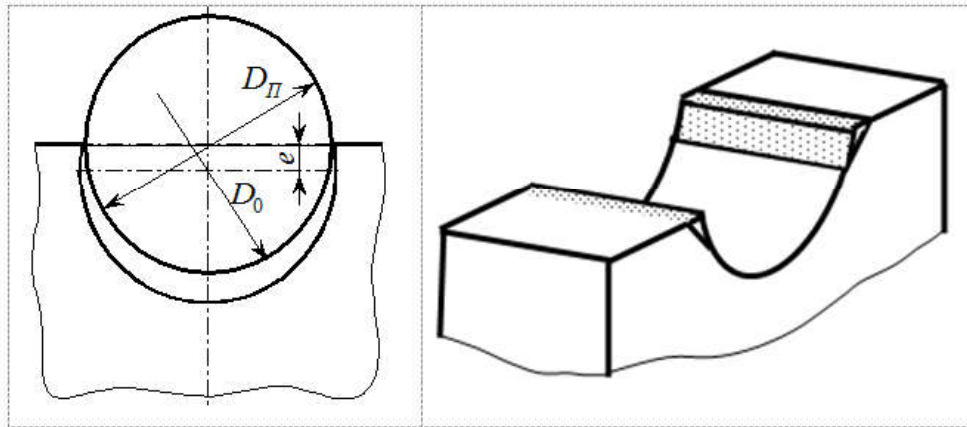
Схема установки зовнішнього кільця вальниці в напівотвір корпусу (а) та припасування поверхонь (б)
